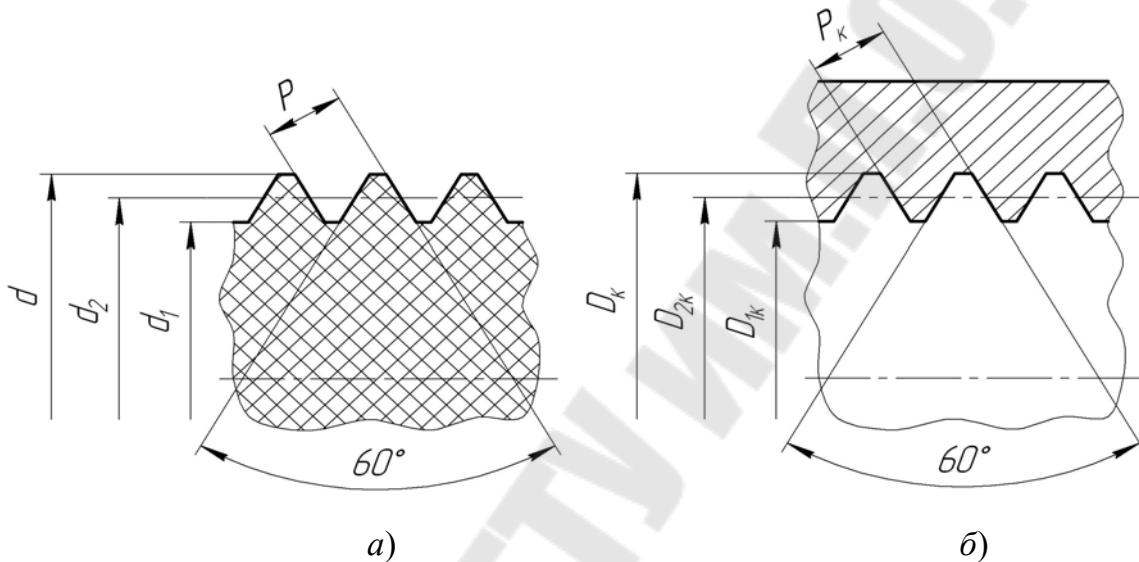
Эскизы: а – болта; б – резьбооформляющего кольца
